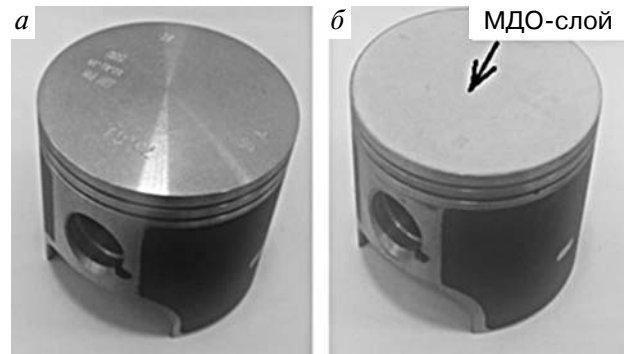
Поршни двигателя PM3-550 до испытаний: а — штатный; б — модифицированный с МДО-слоем
